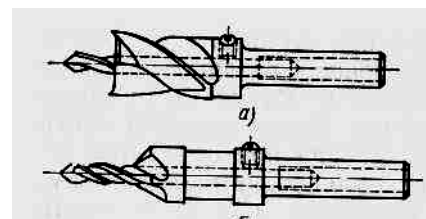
Зенкеры цилиндрический (а) и конический (б)
